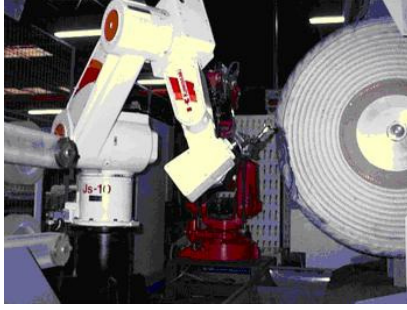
400 F derecedeki Döküm Parçası Kaldırılırken [20]
